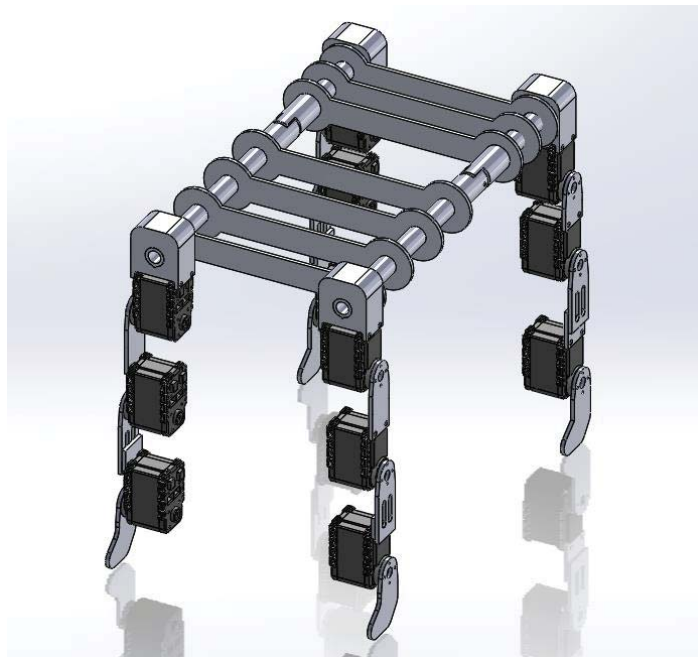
Vista isométrica del robot cuadrúpedo ensamblado.
